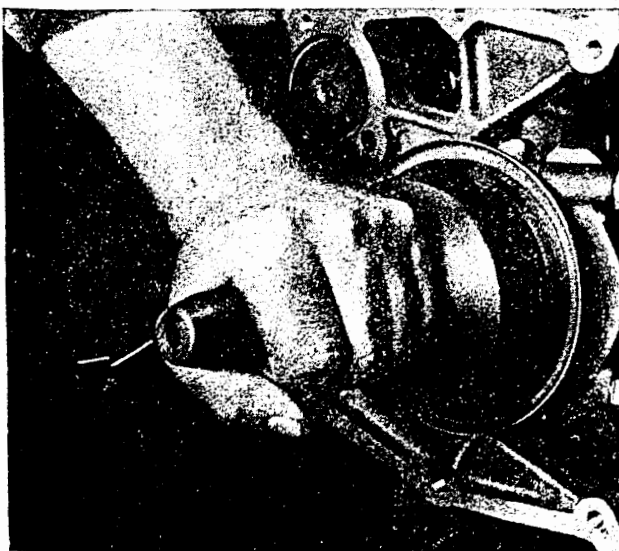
Spritzblech mit Schlagdorn (Werkzeug Nr. 324.020-M 124) auf Kurbelwelle aufschlagen
